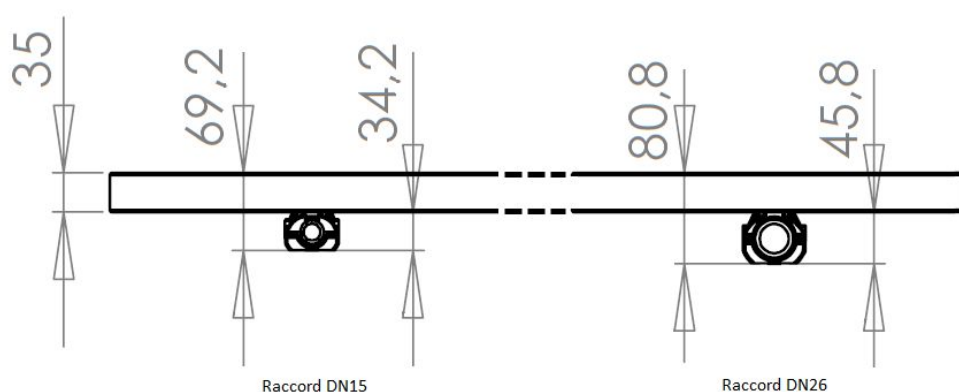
Encombrement des raccords hydrauliques en face arrière
